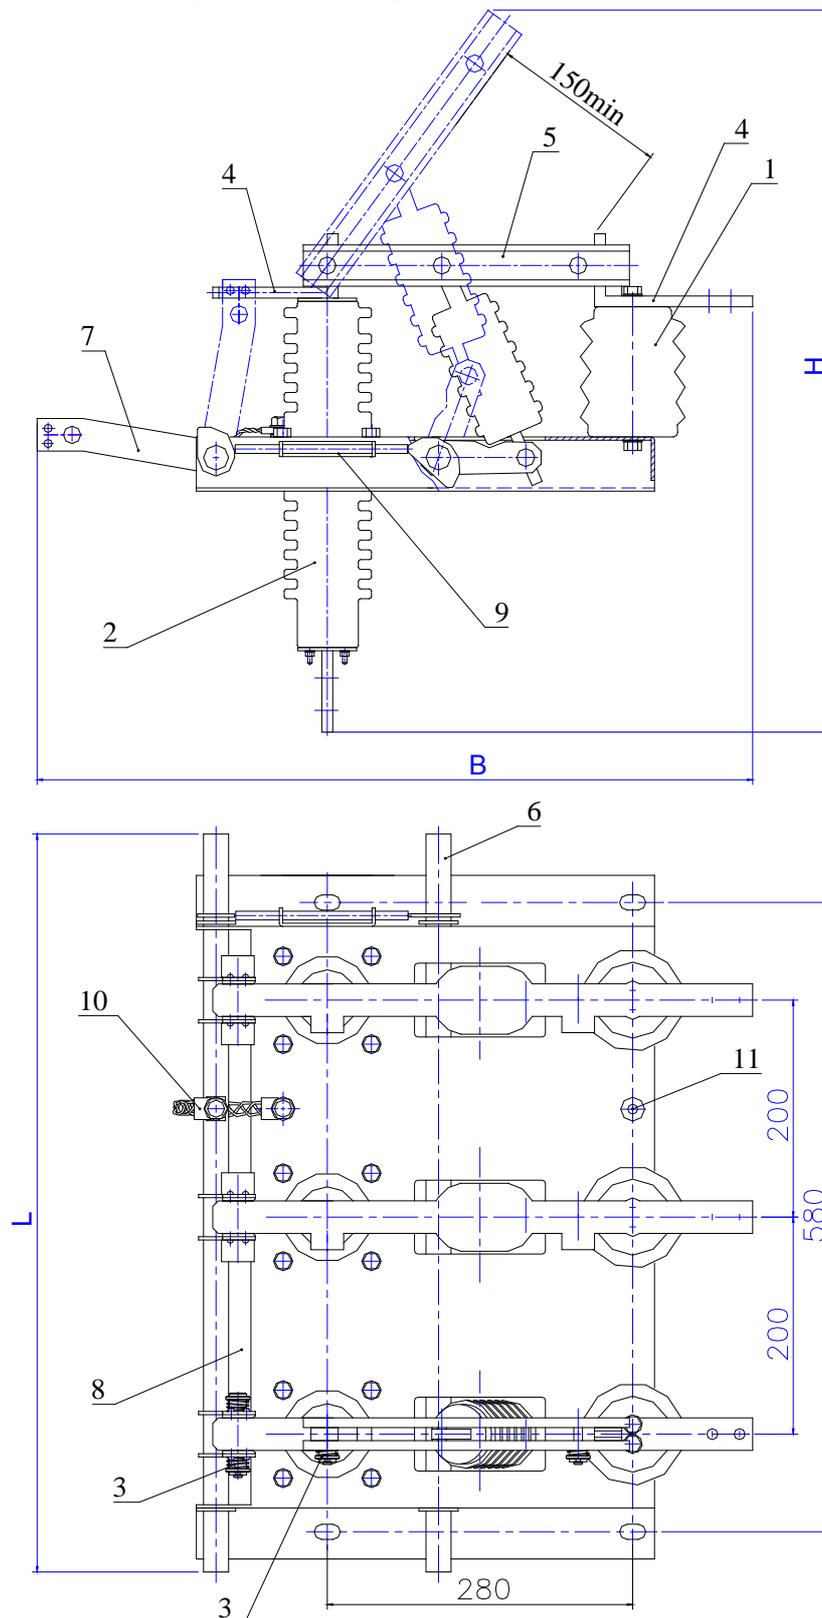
Разъединитель типа РВФ3. 1- изолятор опорный; 2- изолятор проходной; 3- пружина поджатия; 4- неподвижный контакт; 5- подвижный контактный нож; 6- вал разъединителя; 7- заземляющие ножи; 8- вал заземляющих ножей; 9- блокировка; 10- гибкая связь; 11- площадка заземления.
